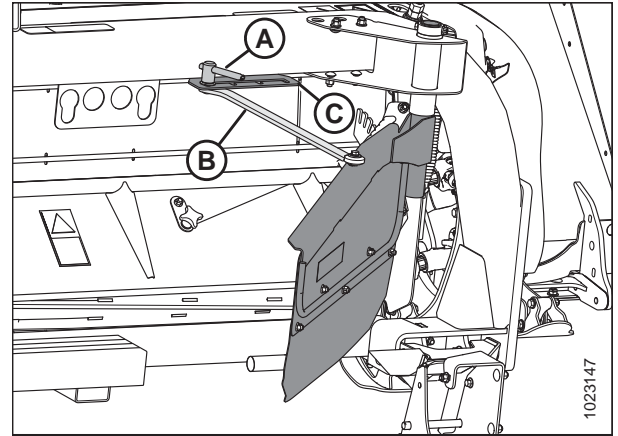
Боковой дефлектор формовочного щитка и регулировочная планка
